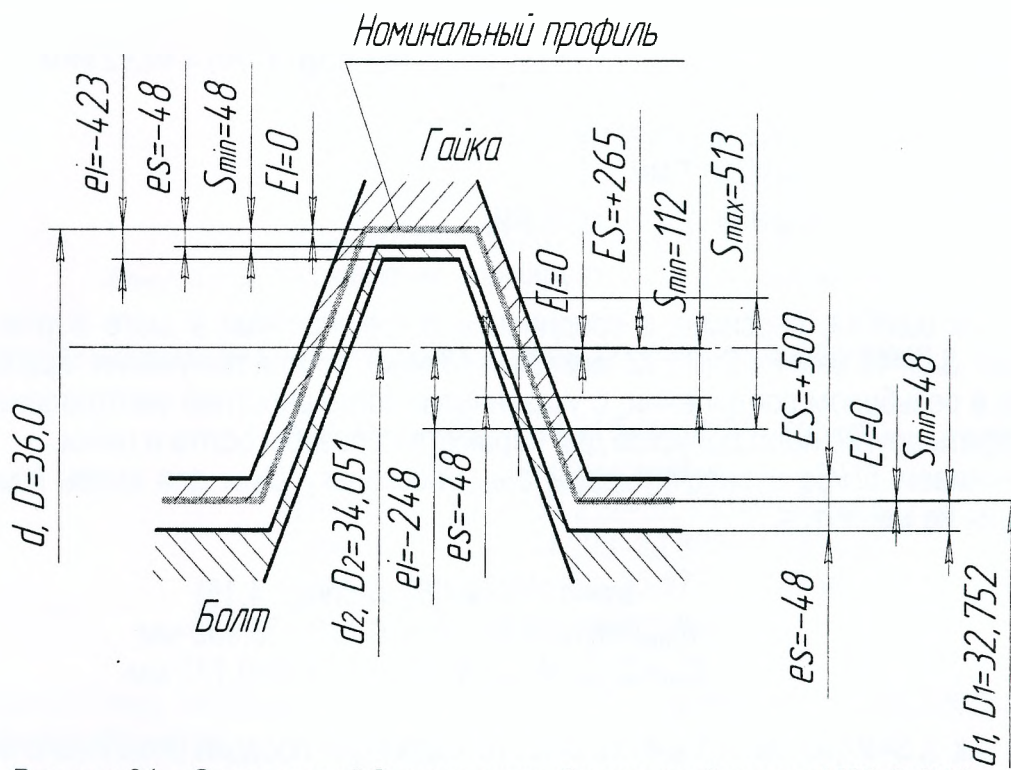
Схема полей допусков резьбового соединения M36x3-6H/6d
